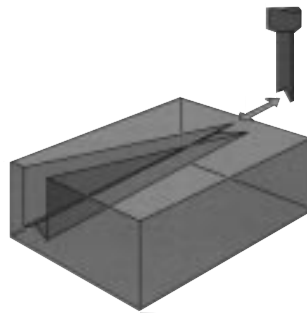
Funkenerosive Bearbeitung entlang einer Linie in 3-D
